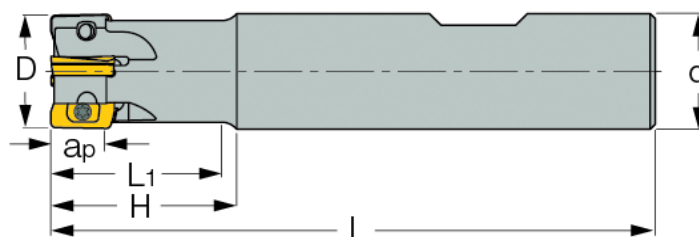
Корпус фрезы E90AN-Д10-1-С10-07-с
